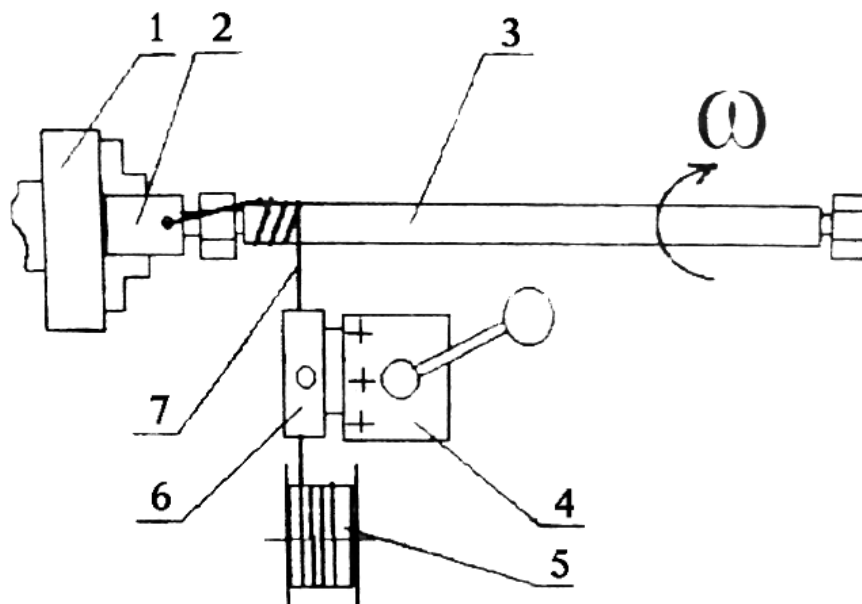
Схема установки для з'єднання шлангу з ніпелем дротом:
